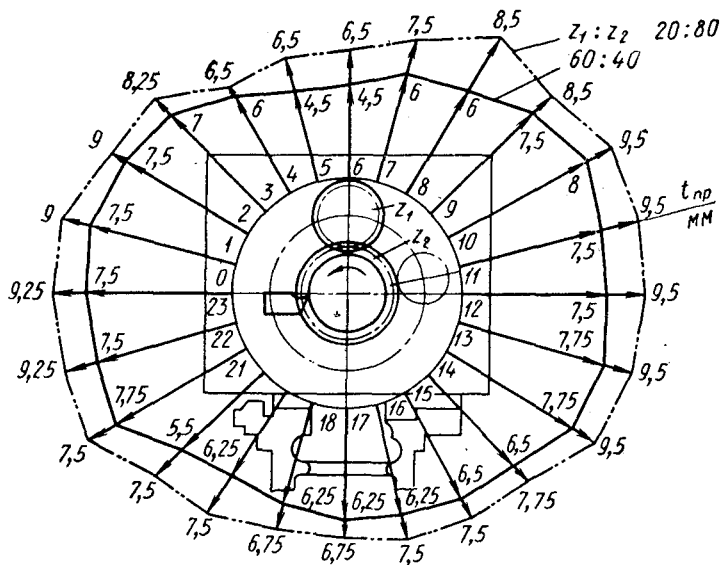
Влияние расположения ведущего зубчатого колеса на величину предельной стружки:
